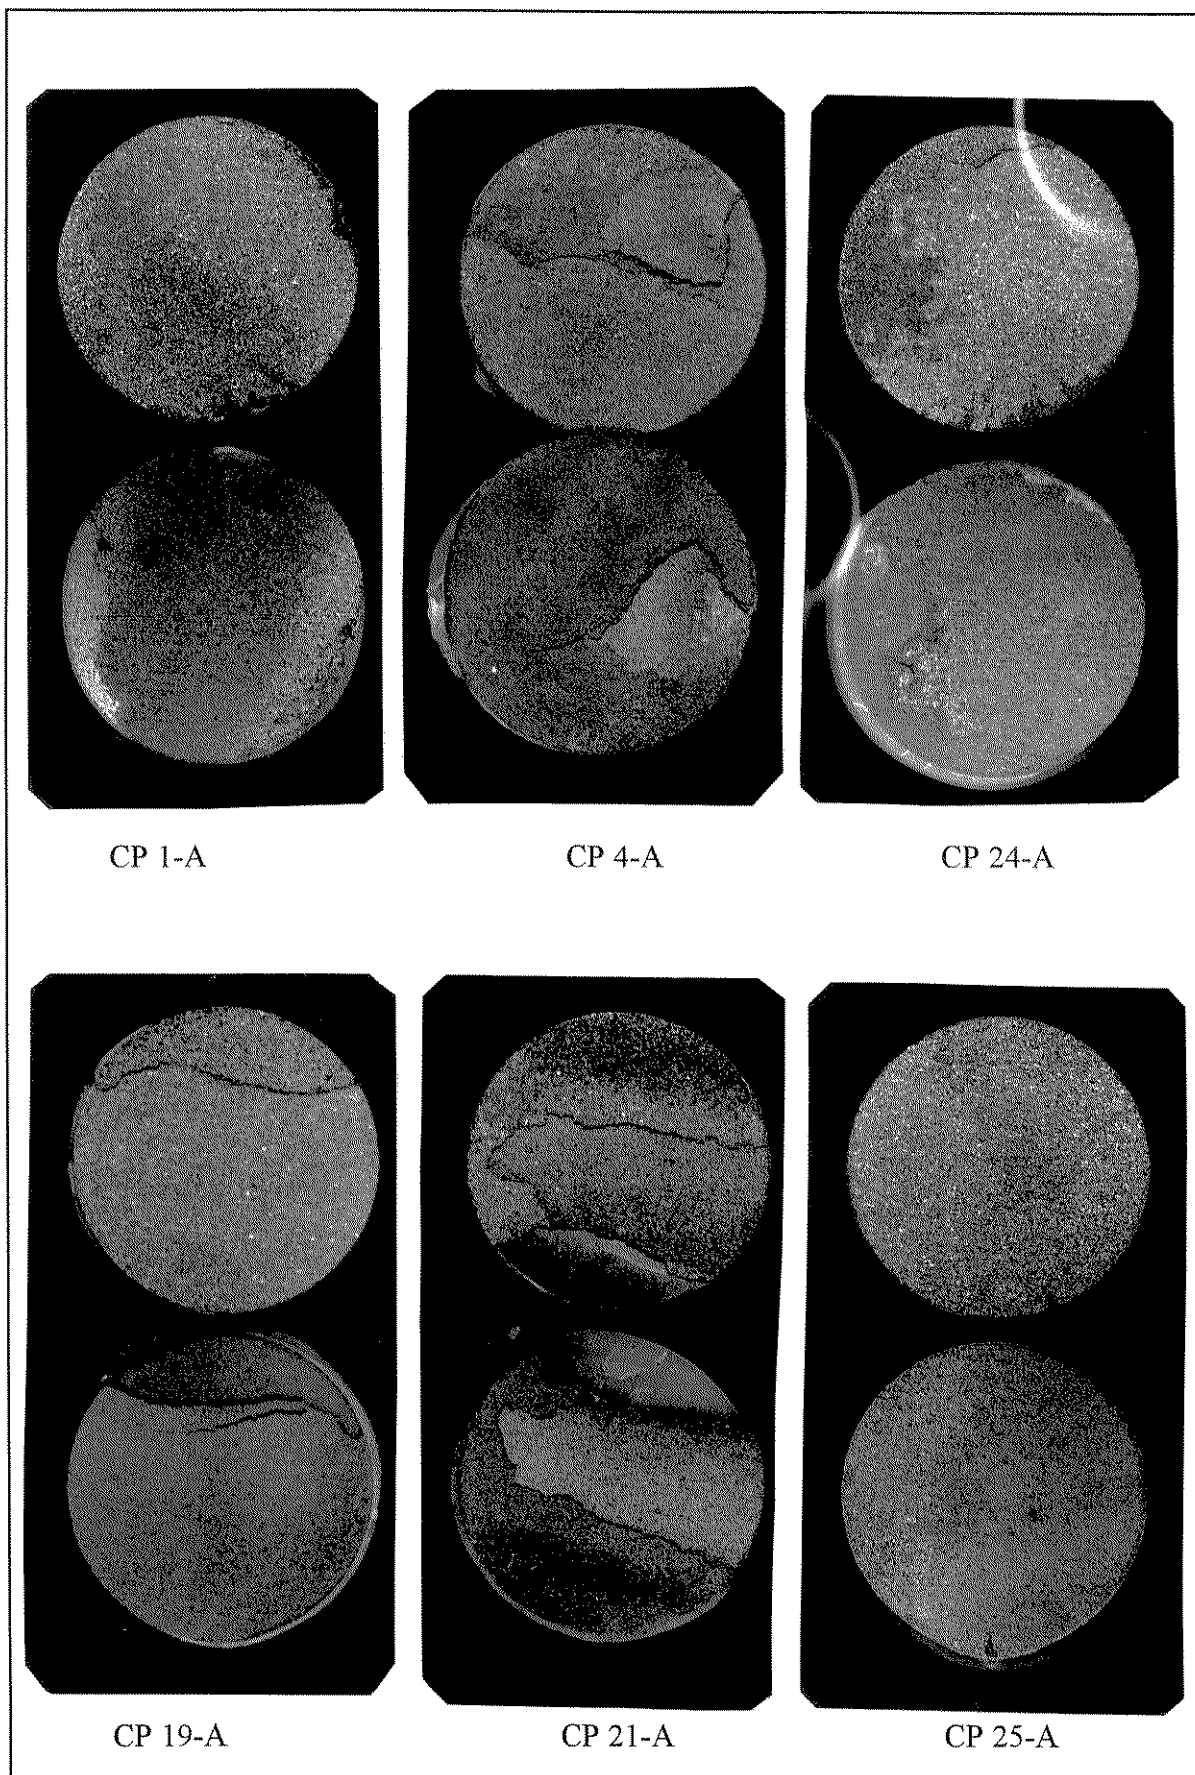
Superfícies de fratura - Ensaio ASTM- C-633 - Base 50-50
